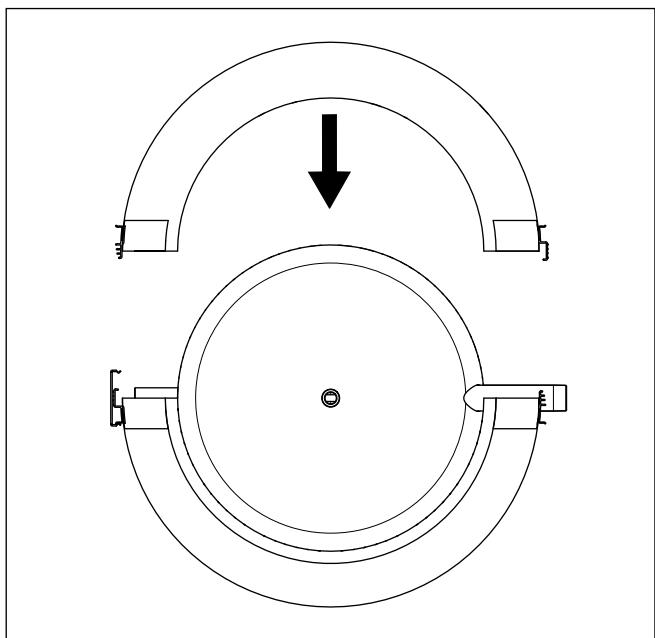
Montage de la demi-coquille droite (par le haut)
